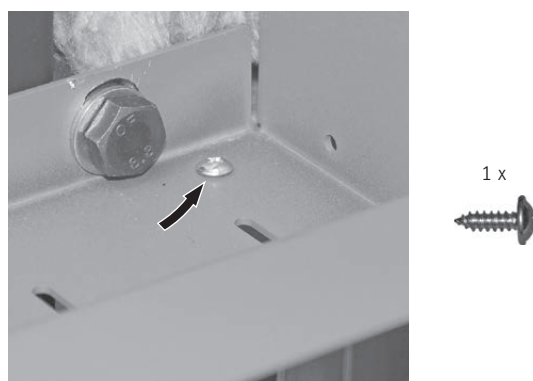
Verkleidungswinkel oben mit Blechschraube festschrauben (nur bei PuroWIN PW 24–60)
